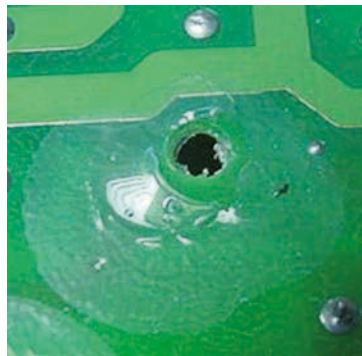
Esempio di pcb con presenza di "sbollature"
